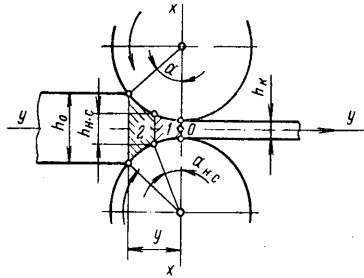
Схема подачі пластичного матеріалу валками
